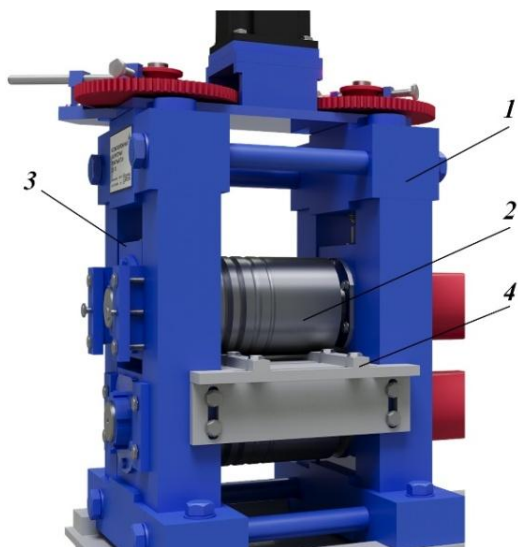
Рабочая клеть прокатного стана ДУО-130: 1 – станина; 2 – универсальные валки; 3 – подушка; 4 – приемно-задающий стол
